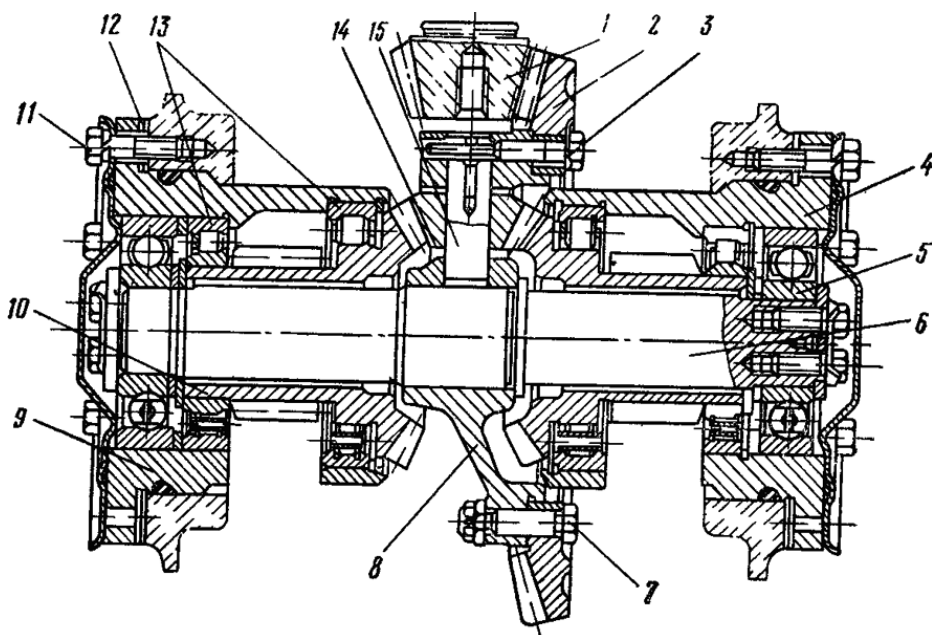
Главная передача и дифференциал. 1 — ведущая шестерня; 2 — венец; 3 — специальный болт; 4, 9 — стаканы подшипников; 5 — шариковые подшипники; 6 — вал главной передачи; 7 — призонный болт; 8 — ступица; 10 — полуосевая шестерня; 11 — болт; 12 — металлические прокладки; 13 — роликовые подшипники; 14 — сателлиты; 15 — ось
